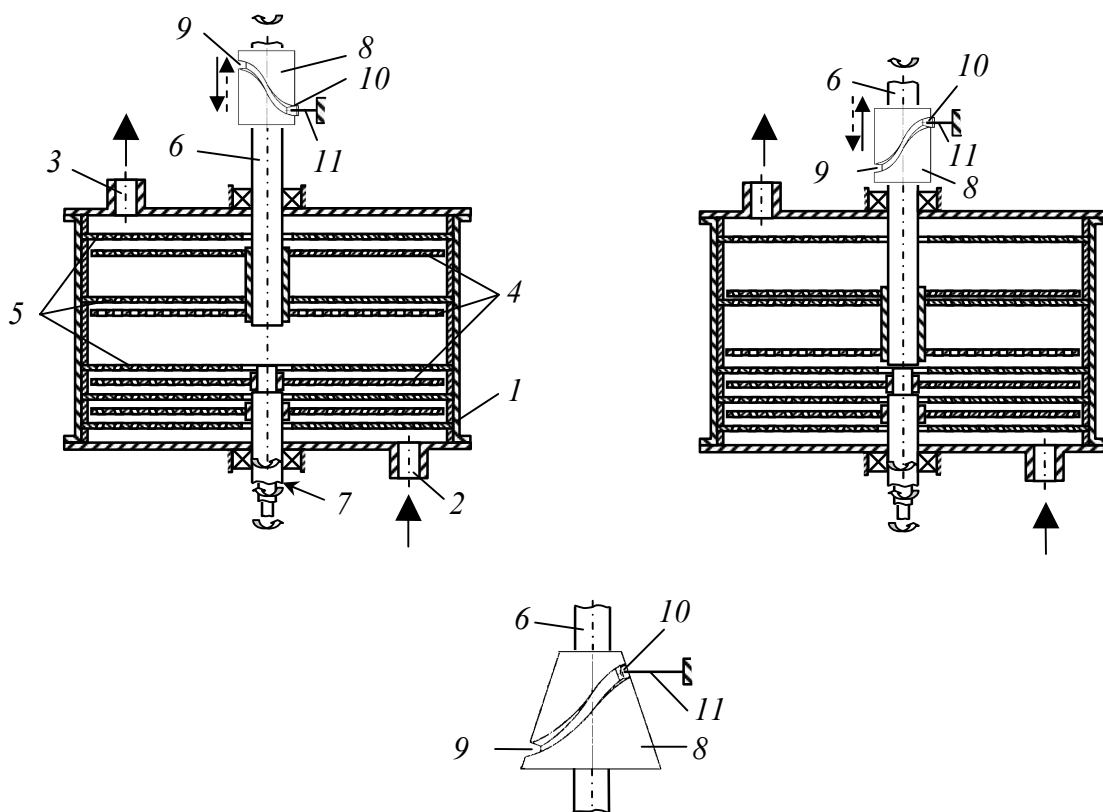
Схема роторно-дискового змішувача згідно з пат. № UA30055U: 1 – корпус; 2, 3 – впускний і випускний патрубки; 4, 5 – перфоровані нерухомі й рухомі диски; 6, 7 – ротори з нерухомими дисками; 8 – кулачок; 9 – замкнений паз; 10 – ролик; 11 – нерухома вісь
